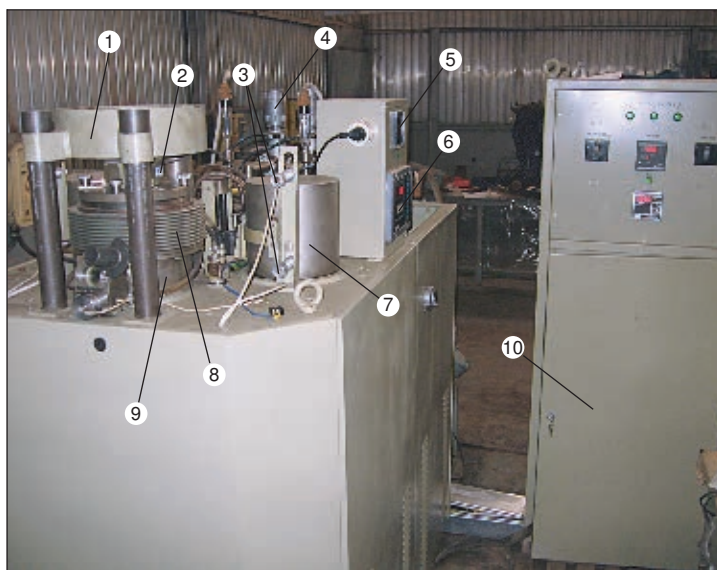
Установка УДС–1 для диффузионной сварки: 1 — силовой упор; 2 — силоизмерительное устройство; 3 — датчики положения камеры загрузки; 4 — элементы вакуумной системы; 5 — датчик температуры; 6 — терминал «ТВ–003/05Д»; 7 — камера загрузки; 8 — сильфонный узел; 9 — камера сварки; 10 — шкаф управления
